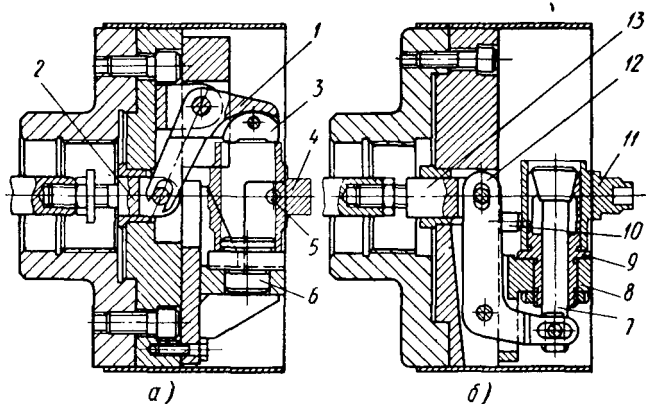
Патроны к токарным и револьверным станкам с зажимом деталей от пневмопривода
